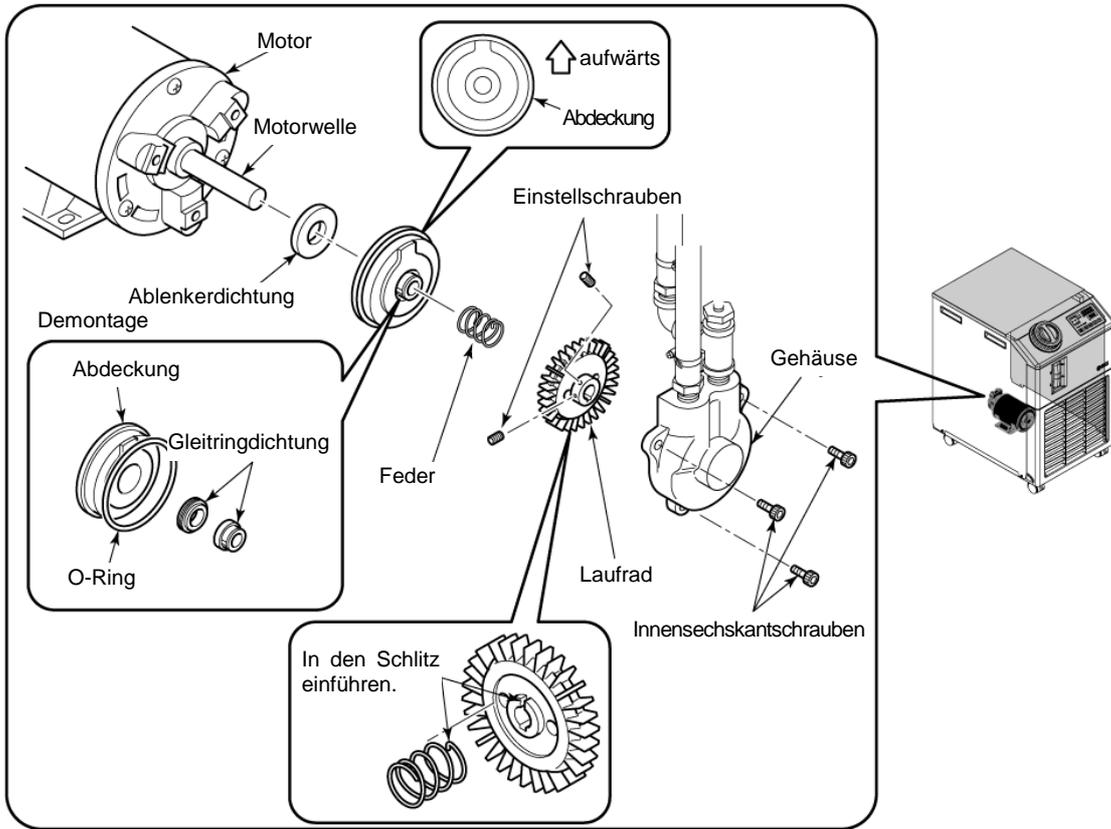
Ausbau des Sets mit mechanischer Dichtung
